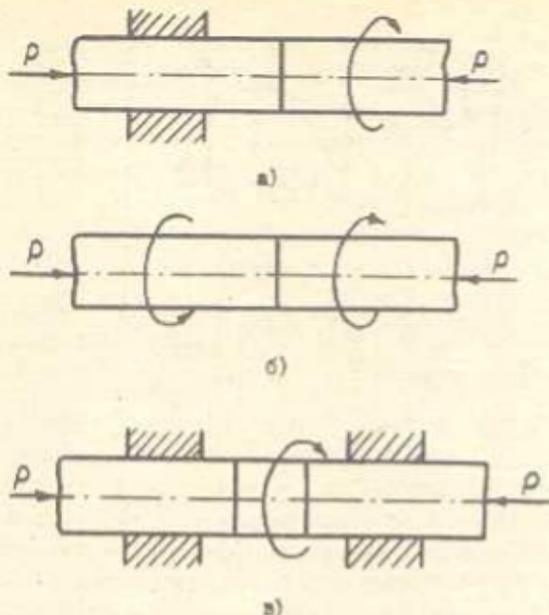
Схема сварки трением: а) при вращении одной детали; б) при вращении обеих деталей; в) при неподвижных деталях с вращающейся вставкой
